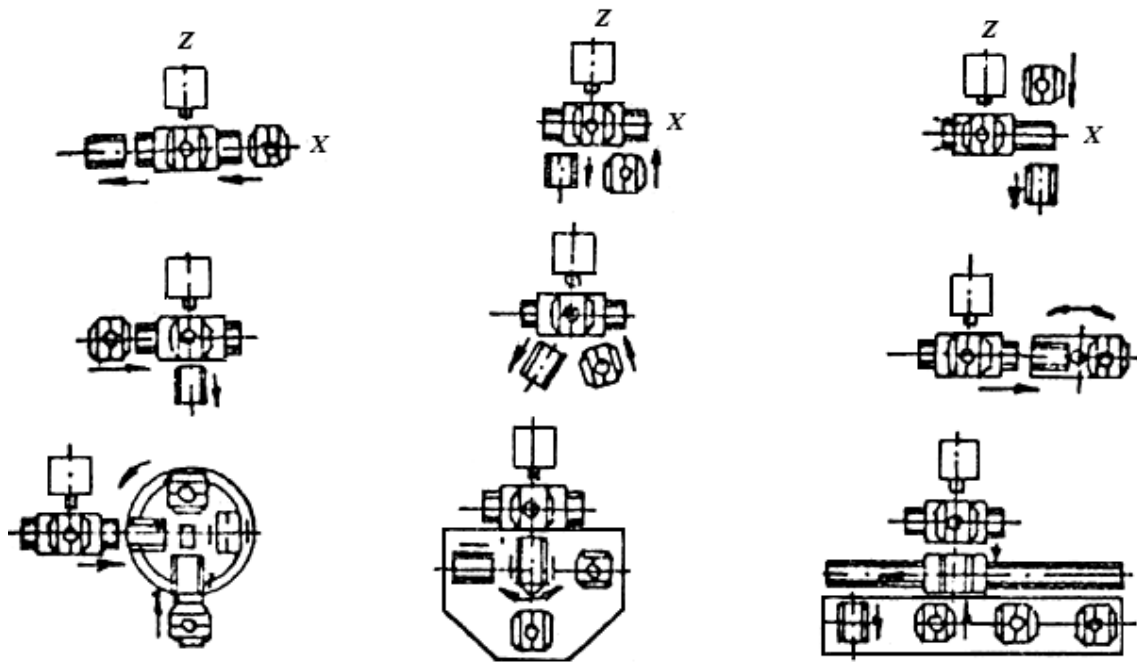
Схеми пристроїв автоматичної зміни заготовок на багатоцільових верстатах
